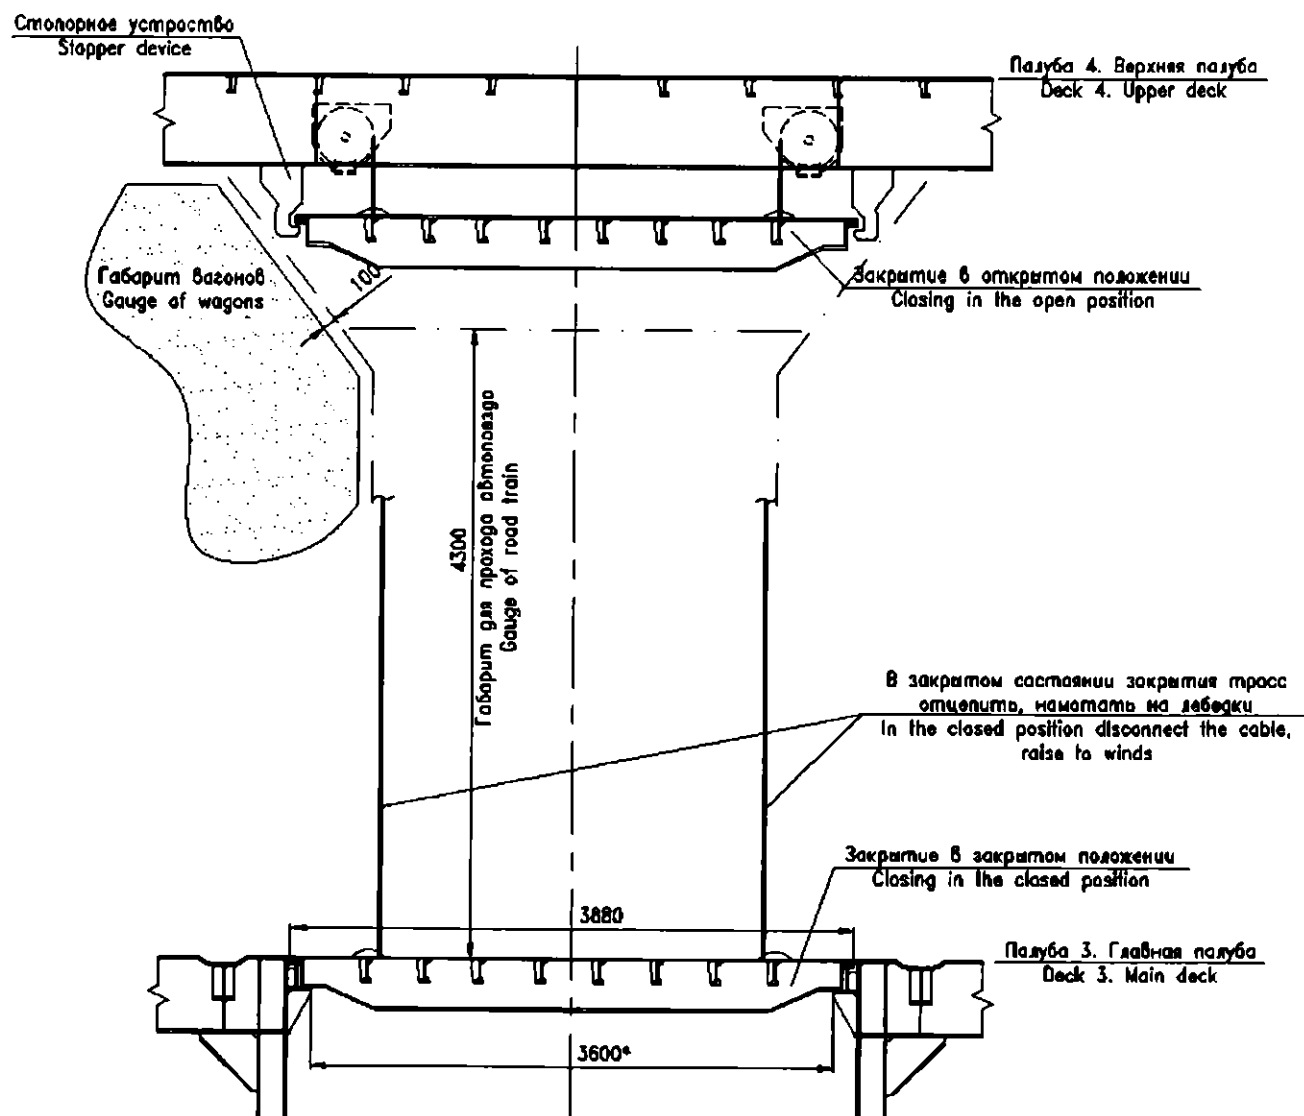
Габаритные размеры поперечный вид / Overall dimensions
